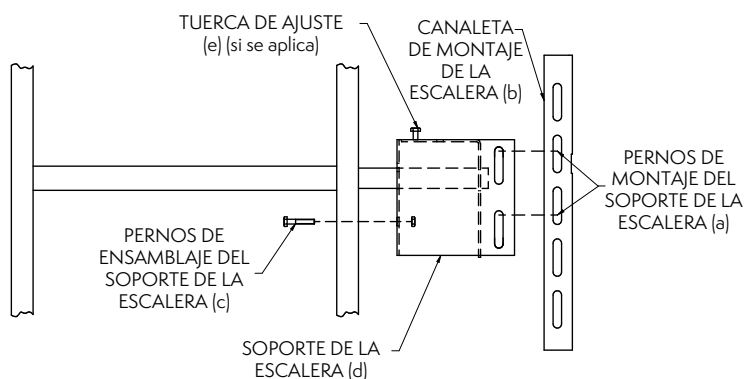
Detalle de la escalera, el soporte de la escalera y la canaleta de montaje
